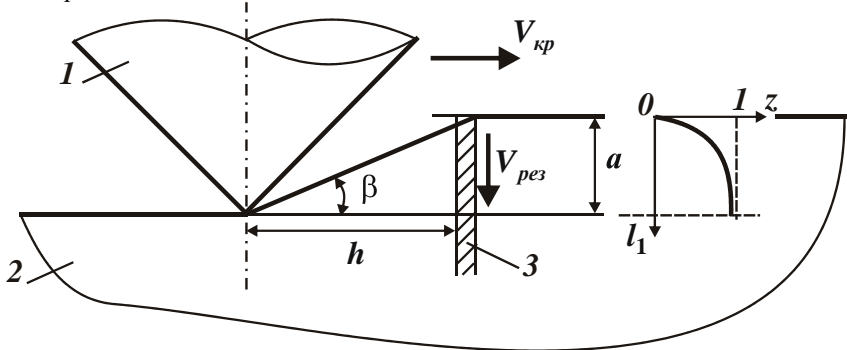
Расчетная схема процесса микрорезания отдельным зерном: 1 – режущее зерно; 2 – обрабатываемый материала; 3 – адиабатический стержень.
